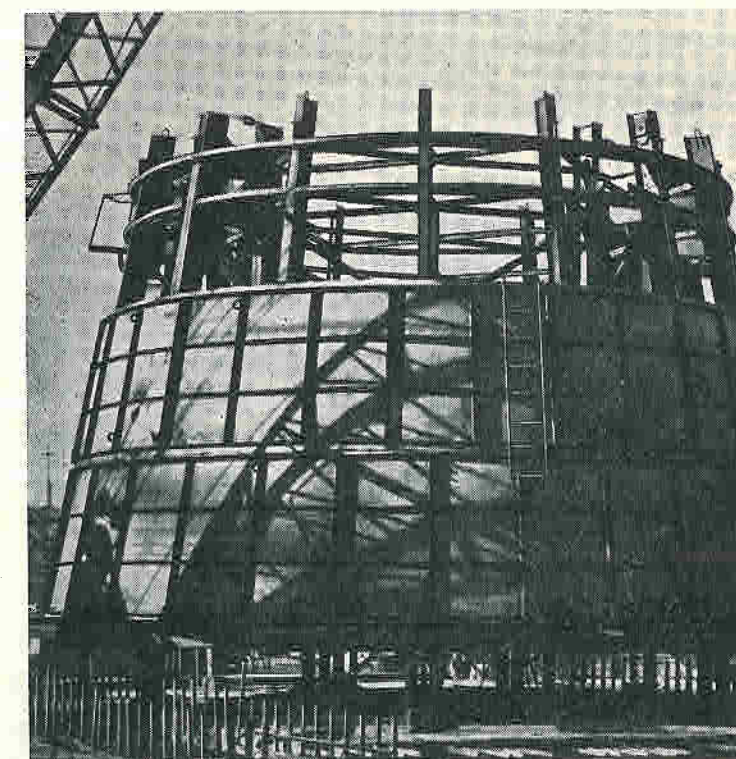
Укрупнительная сборка облицовки конуса гидротурбины на кондукторе
